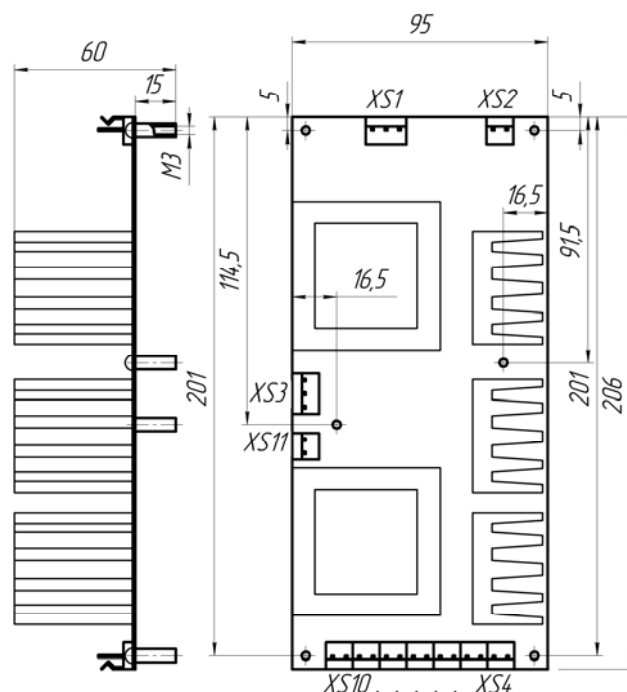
Габаритные и присоединительные размеры ИВЭ-1
